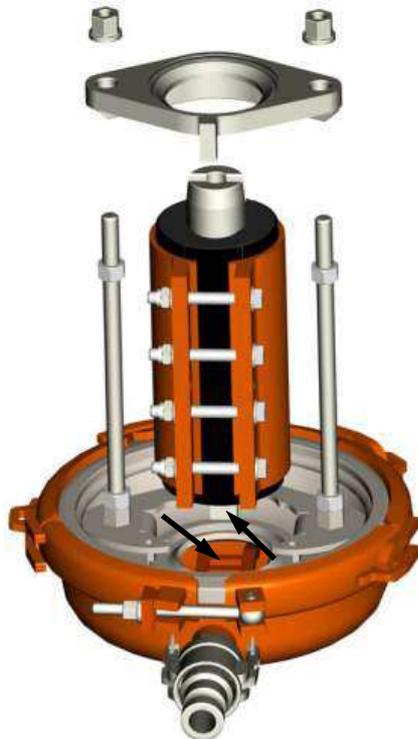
Montar el sistema de bombeo (el muñón del rotor debe introducirse en el alojamiento de la pala mezcladora)
